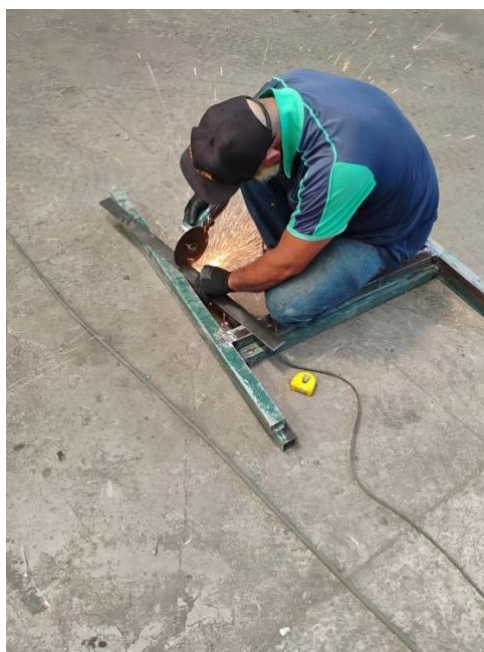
Montagem da estrutura metálica - Fonte: Próprio autor
